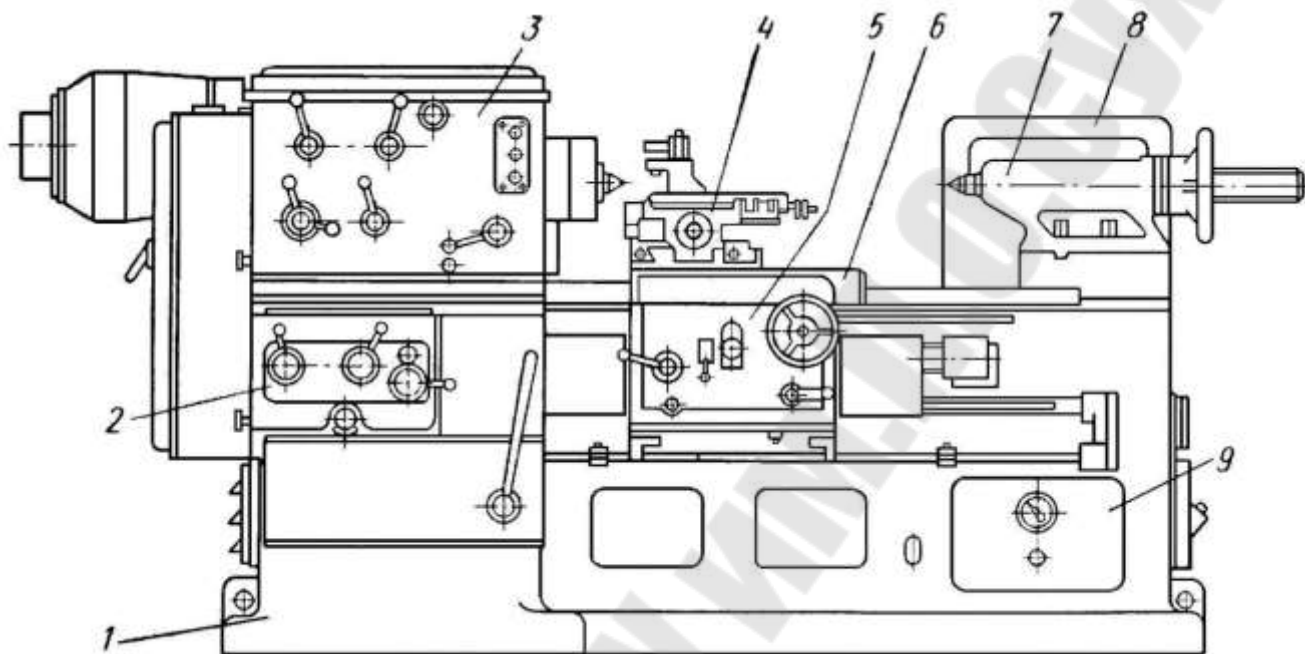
Эскиз общего вида универсального токарно-затыловочного станка модели 1Б811: 1 – станина; 2 – коробка подач; 3 – передняя бабка с коробкой скоростей; 4 – суппорт; 5 – фартук; 6 – каретка; 7 – задняя бабка; 8 – электрошкаф; 9 – гидропривод
